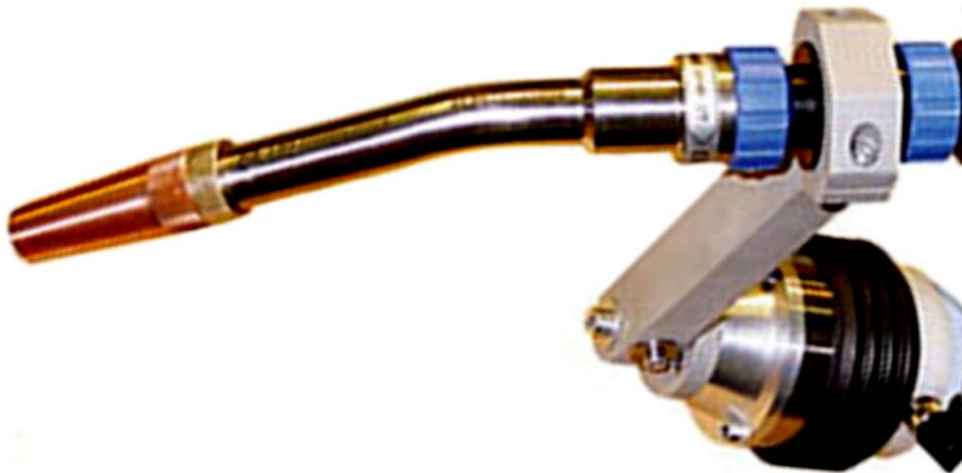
Tocha robotizada para soldagem MIG/MAG.
